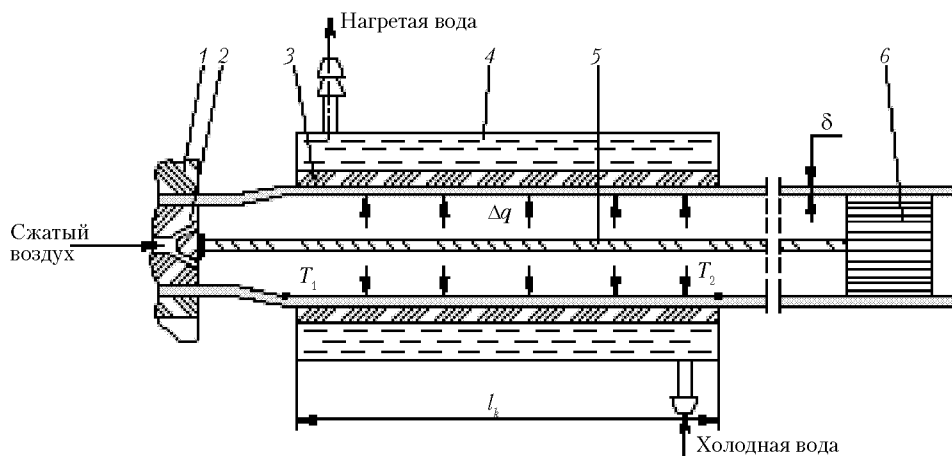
Схема калибрования трубы внутренним давлением  $\Delta q$ : 1 — головка; 2 — экран; 3 — калибрующая втулка; 4 — корпус с охлаждающей водой; 5 — трос; 6 — пробка
